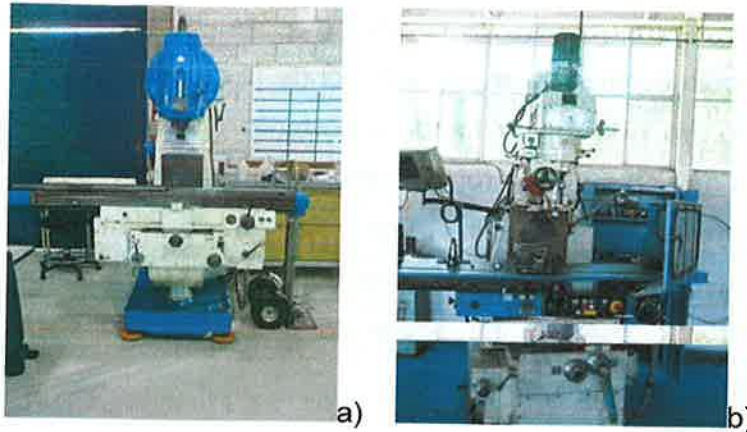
(a) Fresadora TOS OMOLUC, (b) fresadora ARSENAL.
